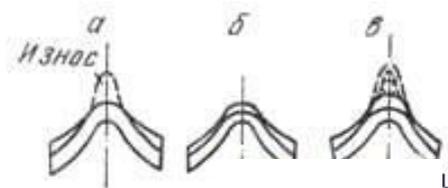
Восстановление зубьев звездочки: а — профиль изношенного зуба; б — наплавка металлическим электродом; в — наплавка комбинированными слоями
